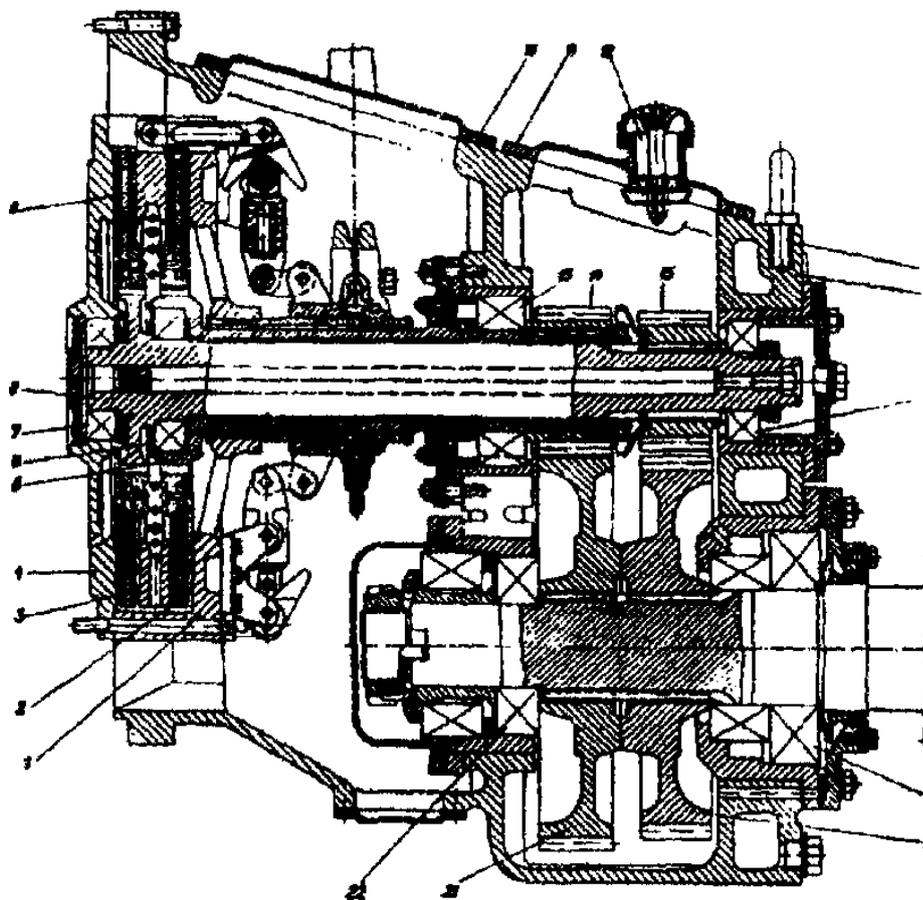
Двухдисковый реверс-редуктор дизеля ЗД6:
